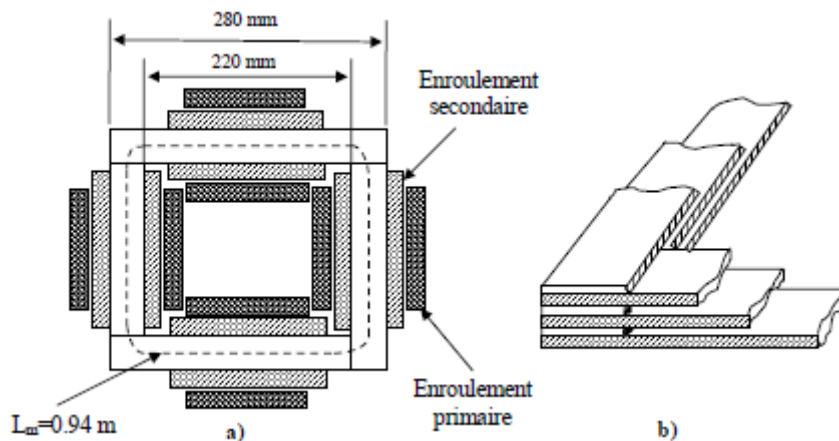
Cadre Epstein, a) dimensions, b) joints de recouvrement
